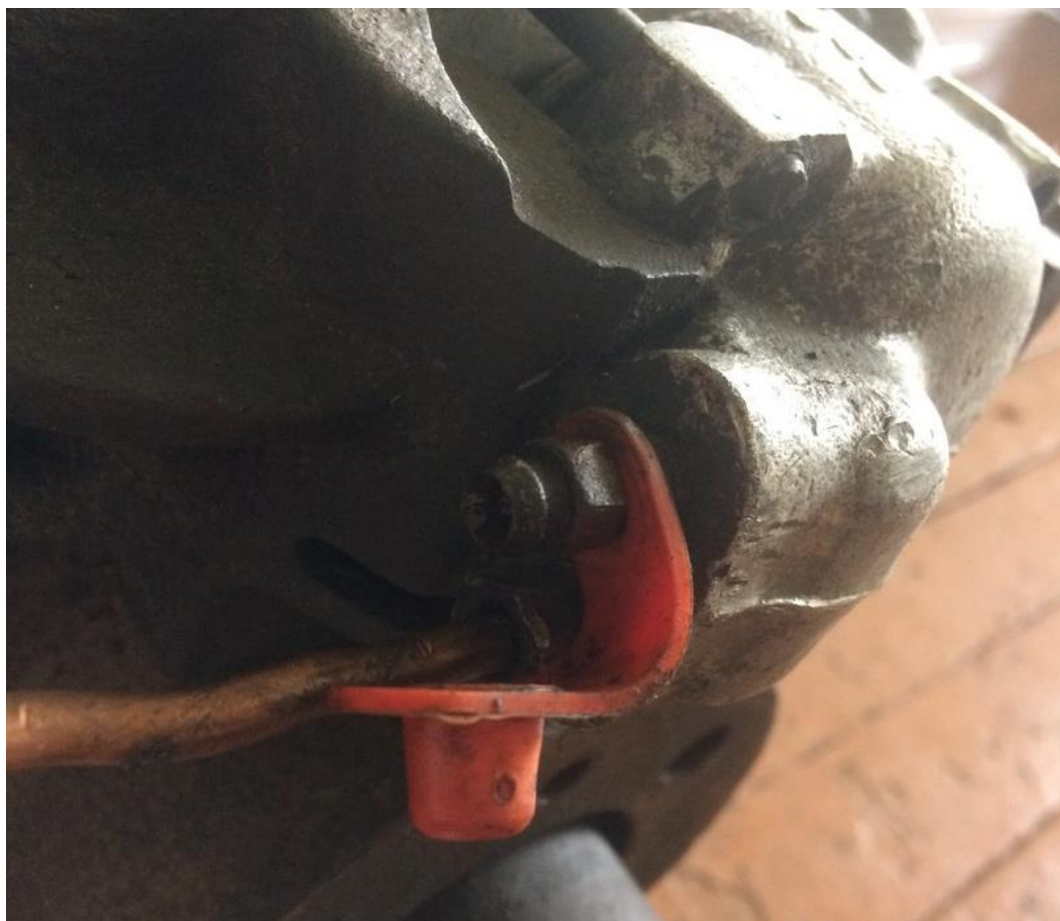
Штуцер для выпуска воздуха переднего колесного цилиндра
